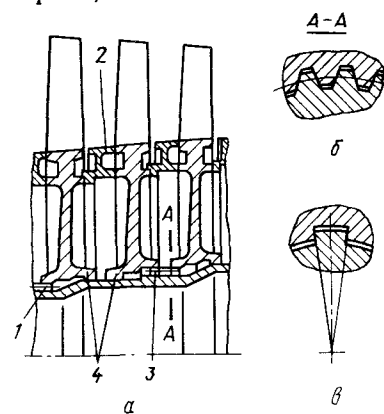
Ротор дискового типа с передачей $M_{кр}$ от вала к дискам шлицами: а — продольный разрез ротора; б — профиль эвольвентных шлиц; в — профиль трапецевидных шлиц (боковые плоскости, образующие трапецевидные поверхности, пересекаются на оси вала); 1, 3 — эвольвентные шлицы; 2 — междисковые проставки; 4 — центрирующие пояски дисков
